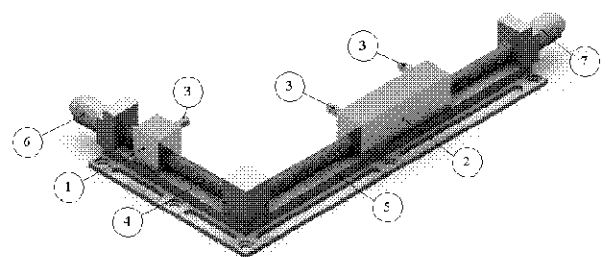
Переналагоджуваний базуючий модуль для установлення корпусних деталей у «координатний кут»
